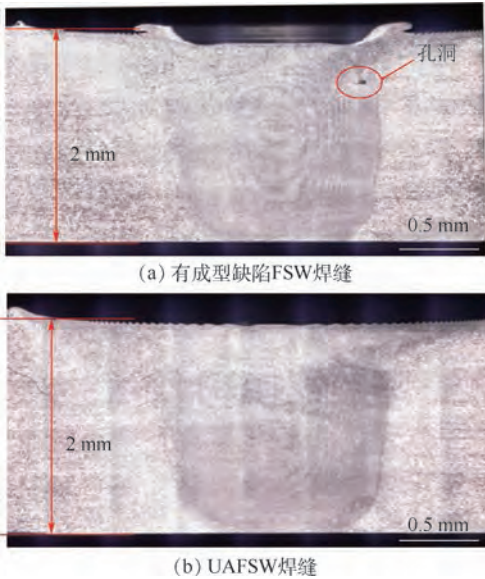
工艺窗口外 FSW 焊缝与 UAFSW 焊缝成型对比
